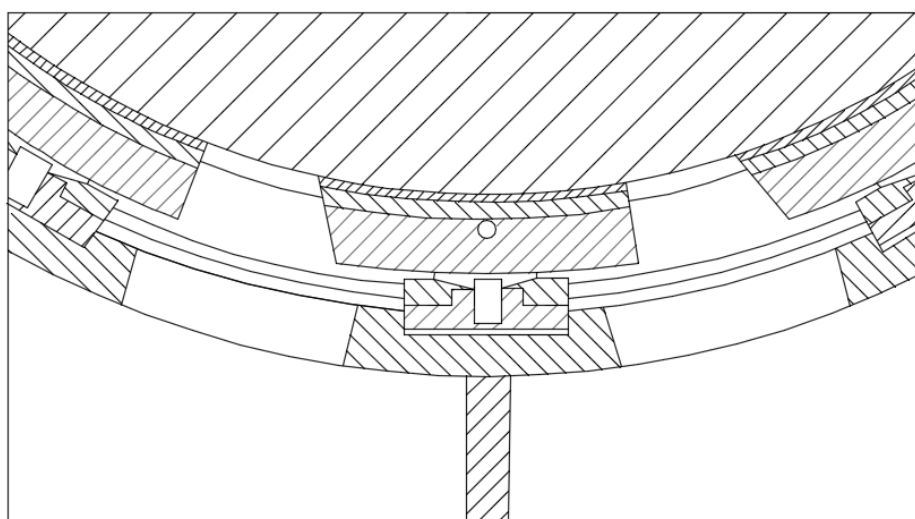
Турбинный подшипник с масляной смазкой СШГЭС
